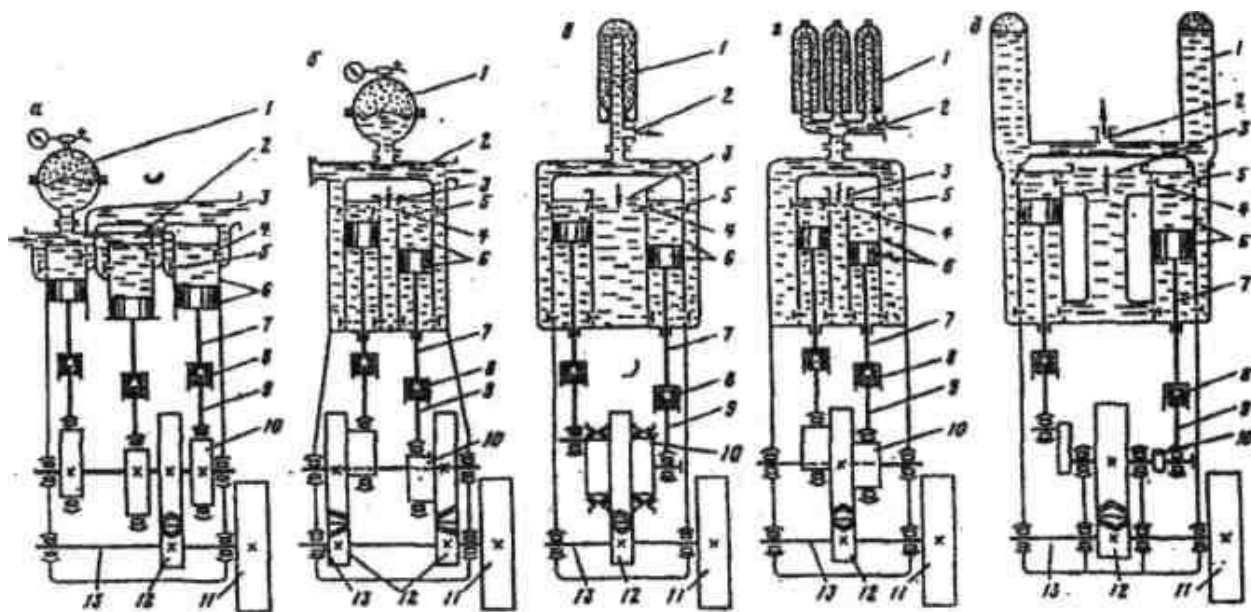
Принципиальные схемы буровых поршневых насосов: 1 - компенсатор; 2,3 - коллекторы выходной и входной; 4,5 - клапаны всасывающий и нагнетательный; 6 - цилиндро-поршневая группа; 7 - шток поршня; 8 - ползун; 9 - шатун; 10 - вал коренной; 11 - шкив; 12 - редуктор зубчатый; 13 - вал трансмиссионный
